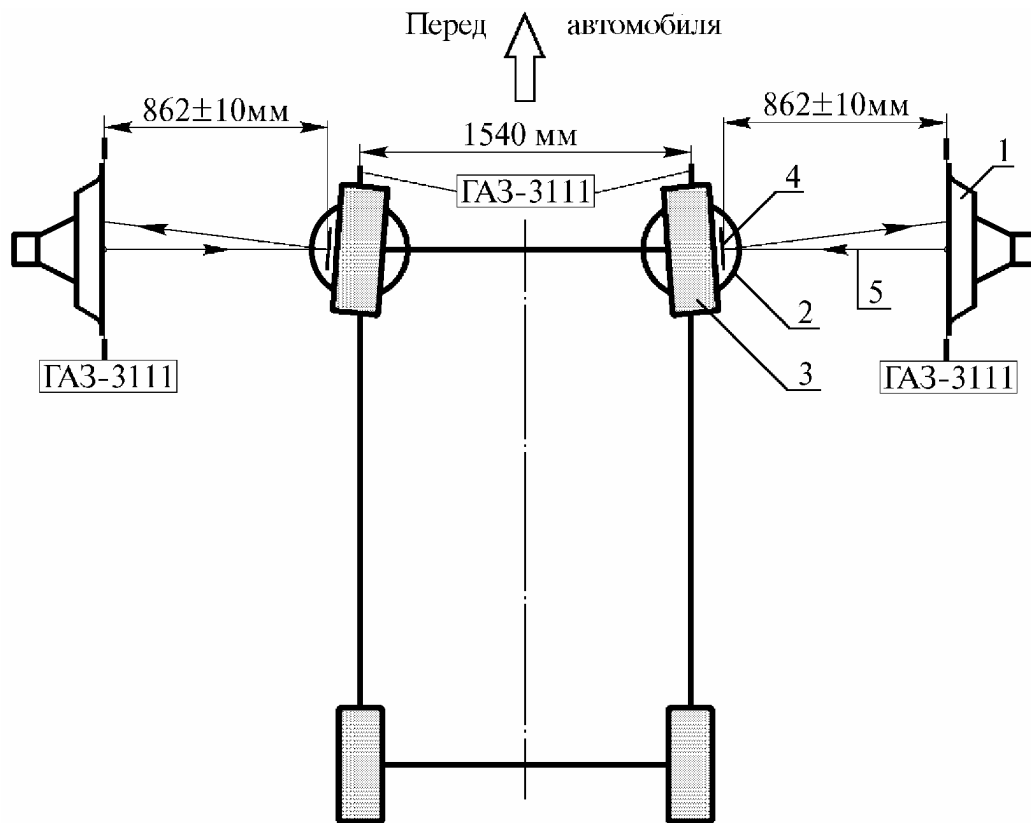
Установка блоков контроля углов и поворотных кругов лазерного устройства для проверки углов установки управляемых колес автомобилей ГАЗ-3111 и модификаций:
